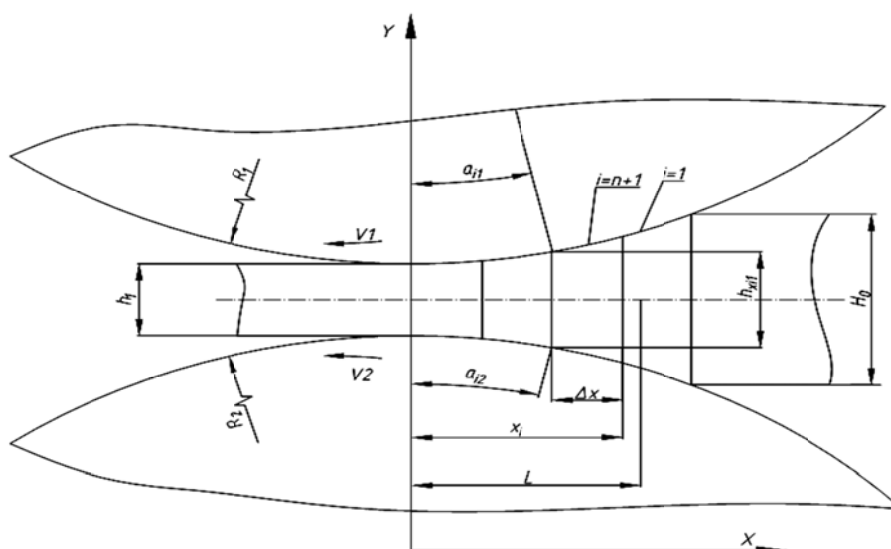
Общий вид расчётной схемы очага деформации при горячей прокатке сварных швов
